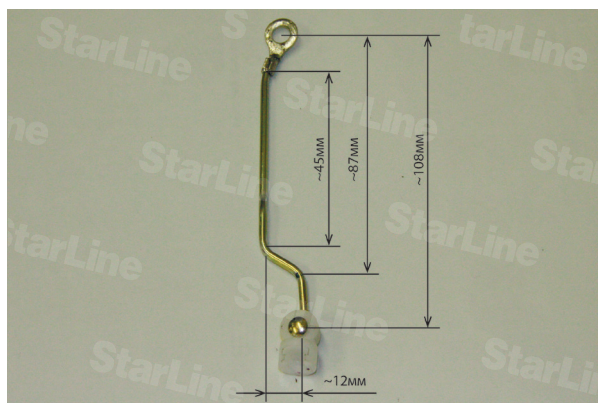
Тяга привода передней левой двери (вид сверху)
